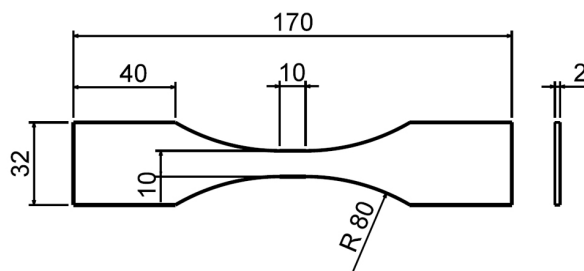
Schéma des éprouvettes et dimensions finales (en mm) après polissage.
